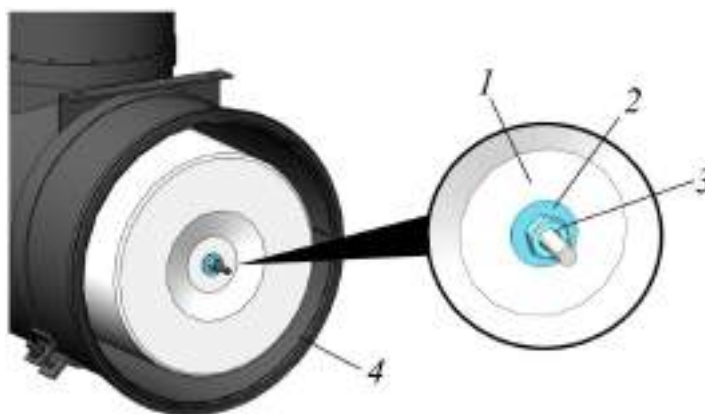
Процедура извлечения из корпуса основного фильтра
